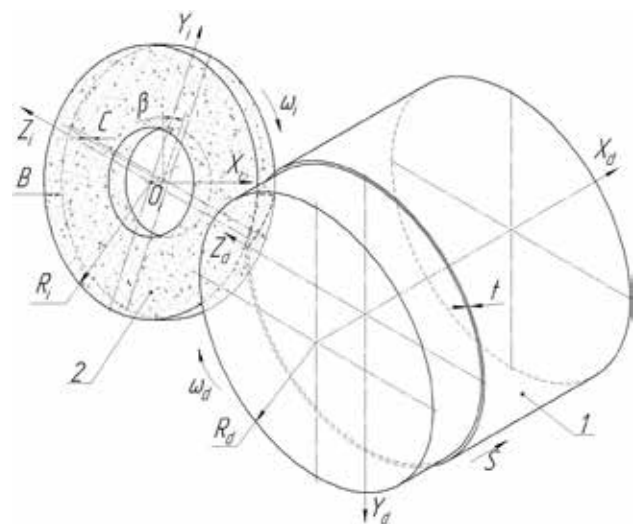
Схема однопрохідного доводочного шліфування циліндричної поверхні валика текстильної машини
